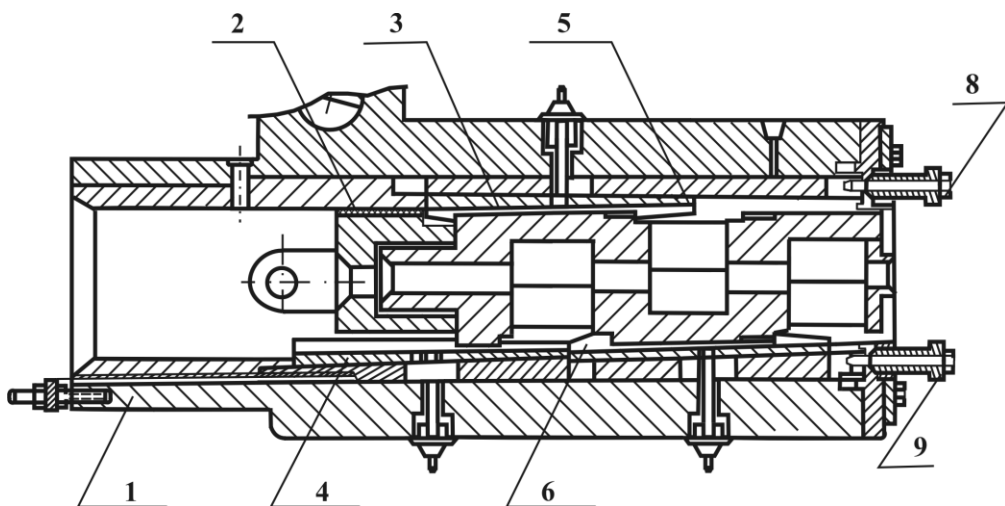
Трирядна кліть для стану ХПТР 8-15: 1 – корпус; 2 – повзун; 3 – сепаратор; 4 – планка третього ряду; 5 – планка другого ряду; 6 – планка першого ряду; 7 – повзун
